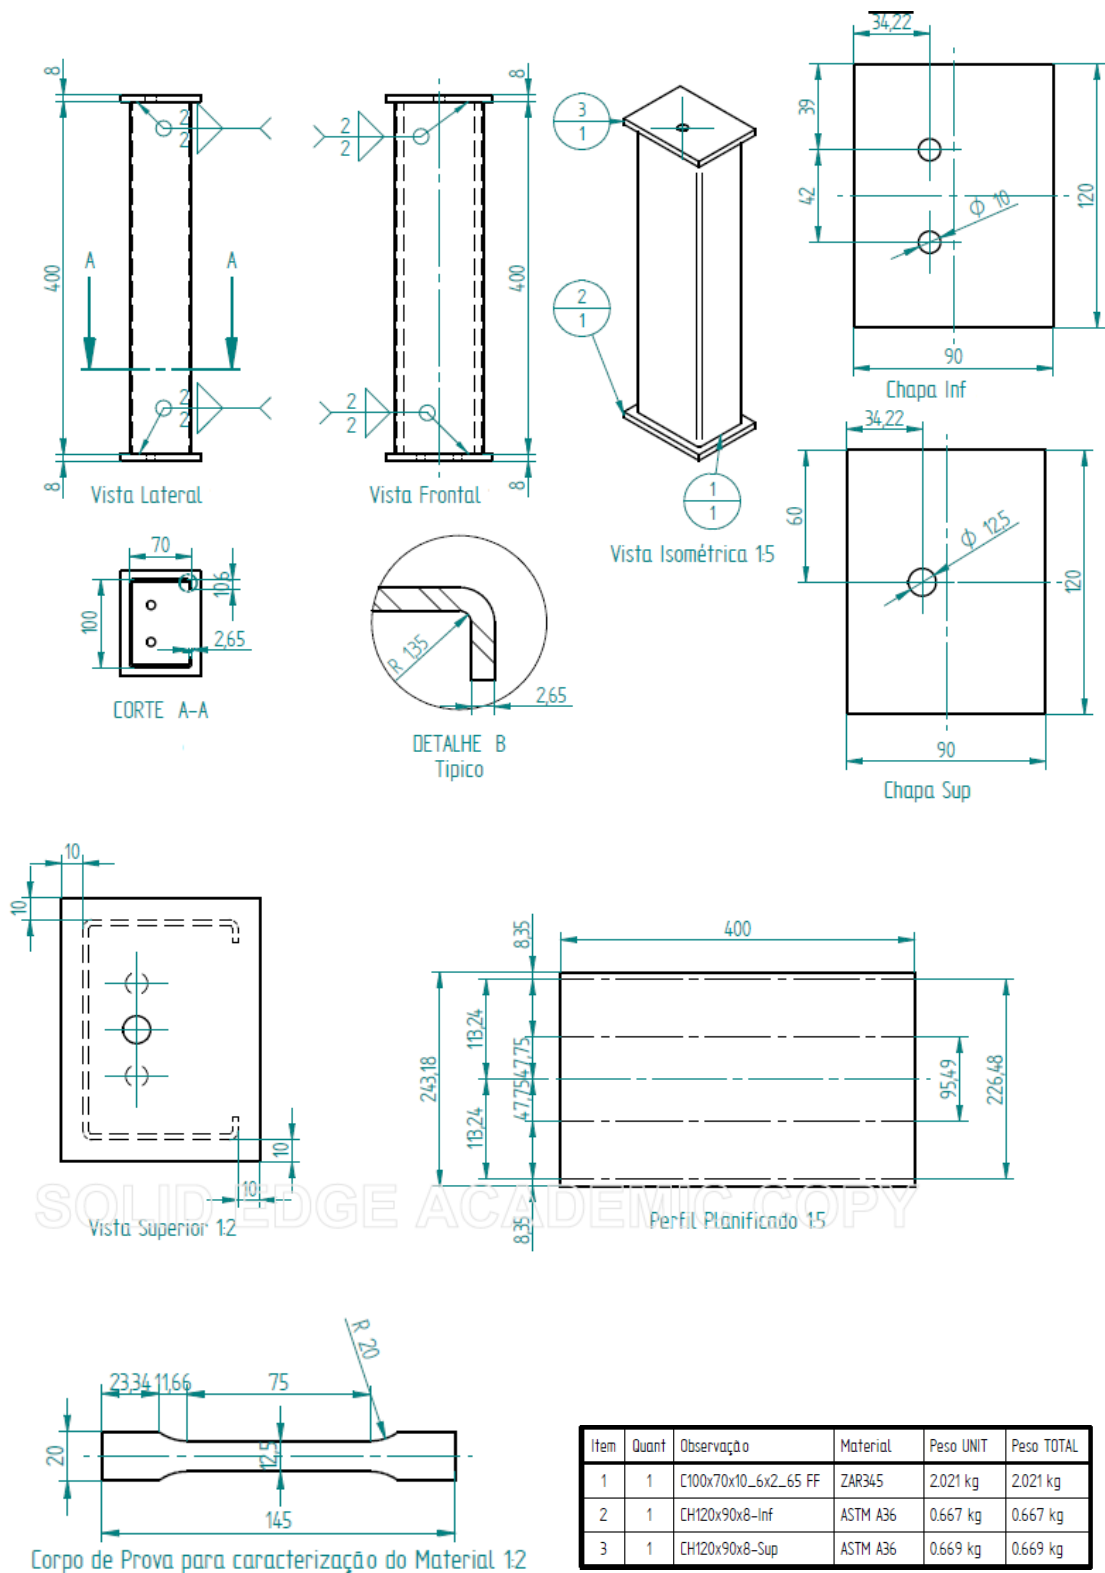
Projeto para fabricação dos PFF (coluna C100x70FF400).
